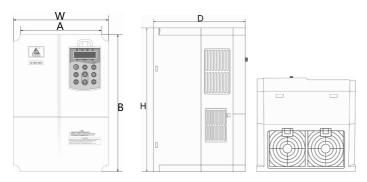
PV6000 塑胶结构外型尺寸及安装尺寸示意图
